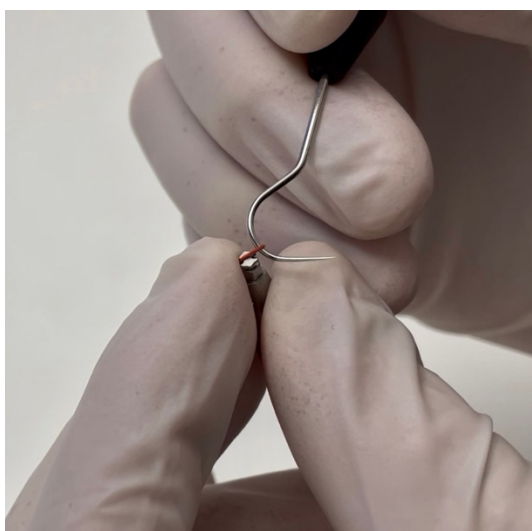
Aufziehen des fixierten O-Rings auf das Einbringtool
